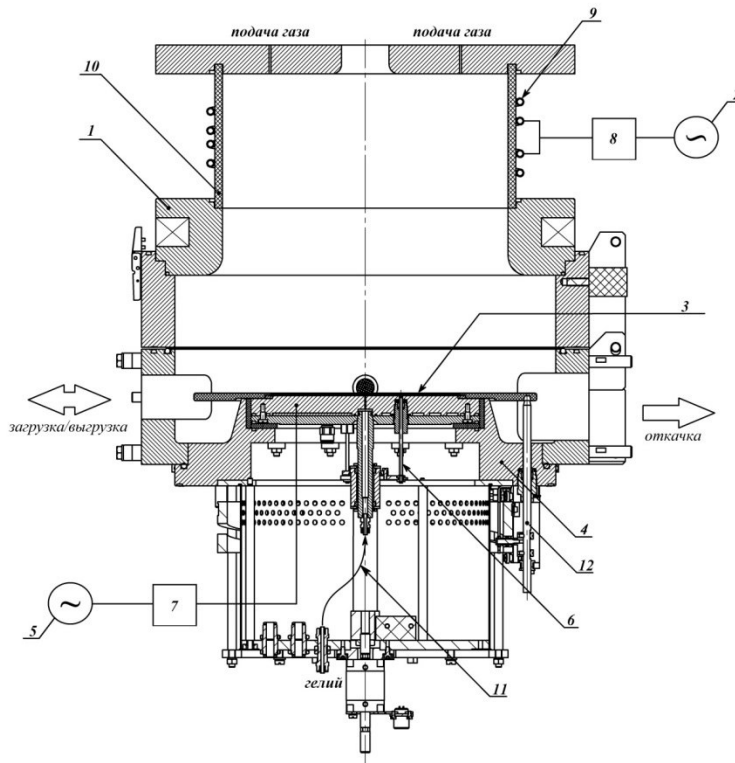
Конструкция реактора установки для Bosch-процесса.
